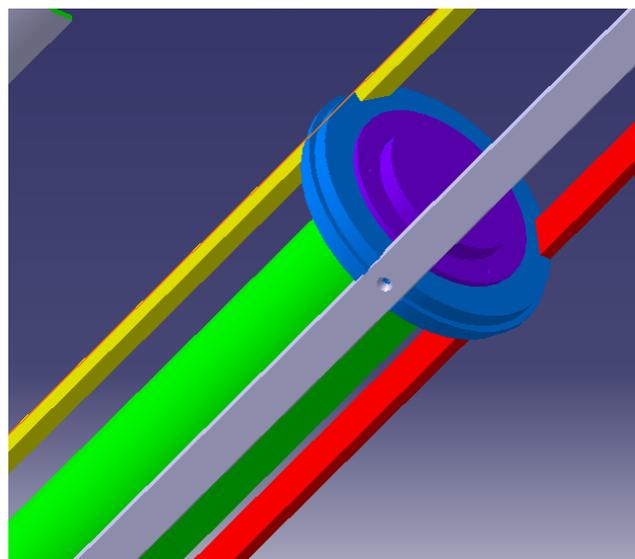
Présentation de la plaque de poussée et du bouchon moteur assemblés
